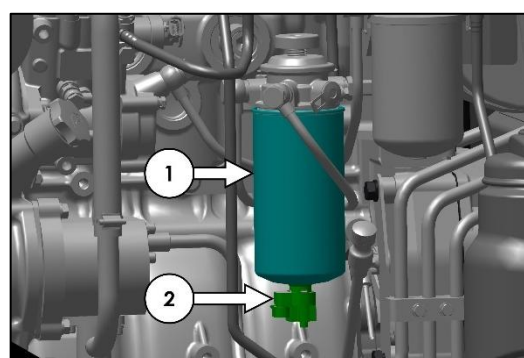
ASSEMBLAGE DU FILTRE À CARBURANT
